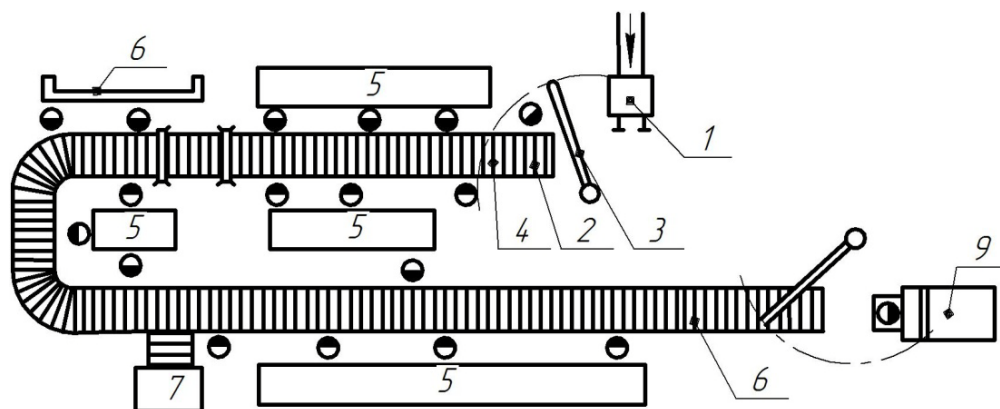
Схема планировки сборочного участка при применении роликового конвейера: 1 – подача базовой детали; 2 – начало сборки; 3 – кран-укосина; 4 – рольганг; 5 – верстаки; 6 – стеллажи; 7 – место для выполнения пригоночной операции; 8 – конец сборки; 9 – передача собранного изделия на транспорт
